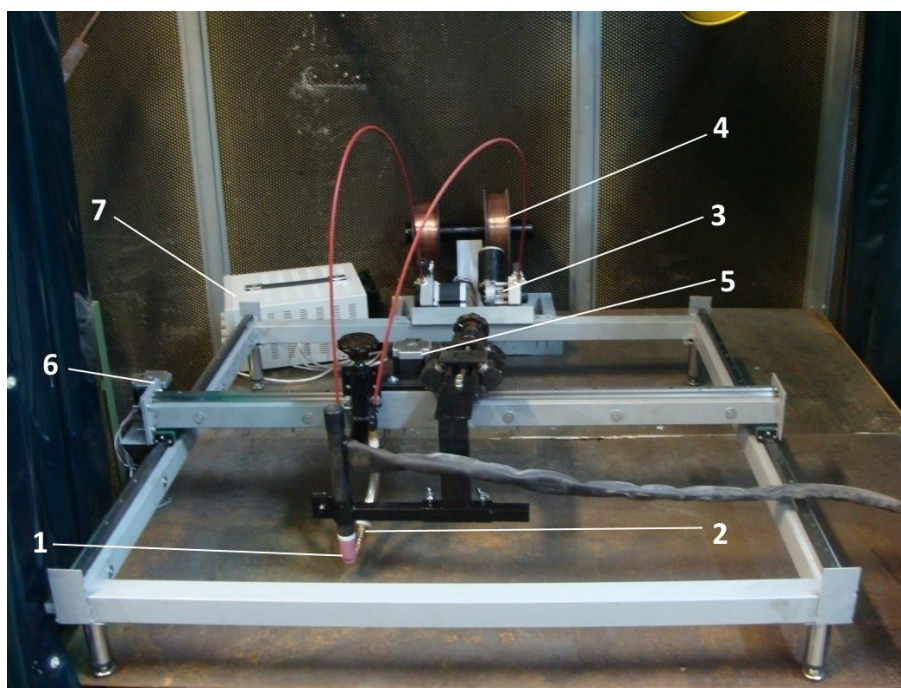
Установка для автоматической аргодуговой наплавки неплавящимся электродом: 1 – горелка для сварки неплавящимся электродом; 2 – мундштук для подачи присадочной проволоки; 3 – Механизм подачи присадочной проволоки; 4 – Бухта с алюминиевой присадочной проволокой, закрепленная на станине; 5 – Шаговый двигатель для перемещения по оси X; 6 – Шаговый двигатель для перемещения по оси Y; 7 – блок управления.
